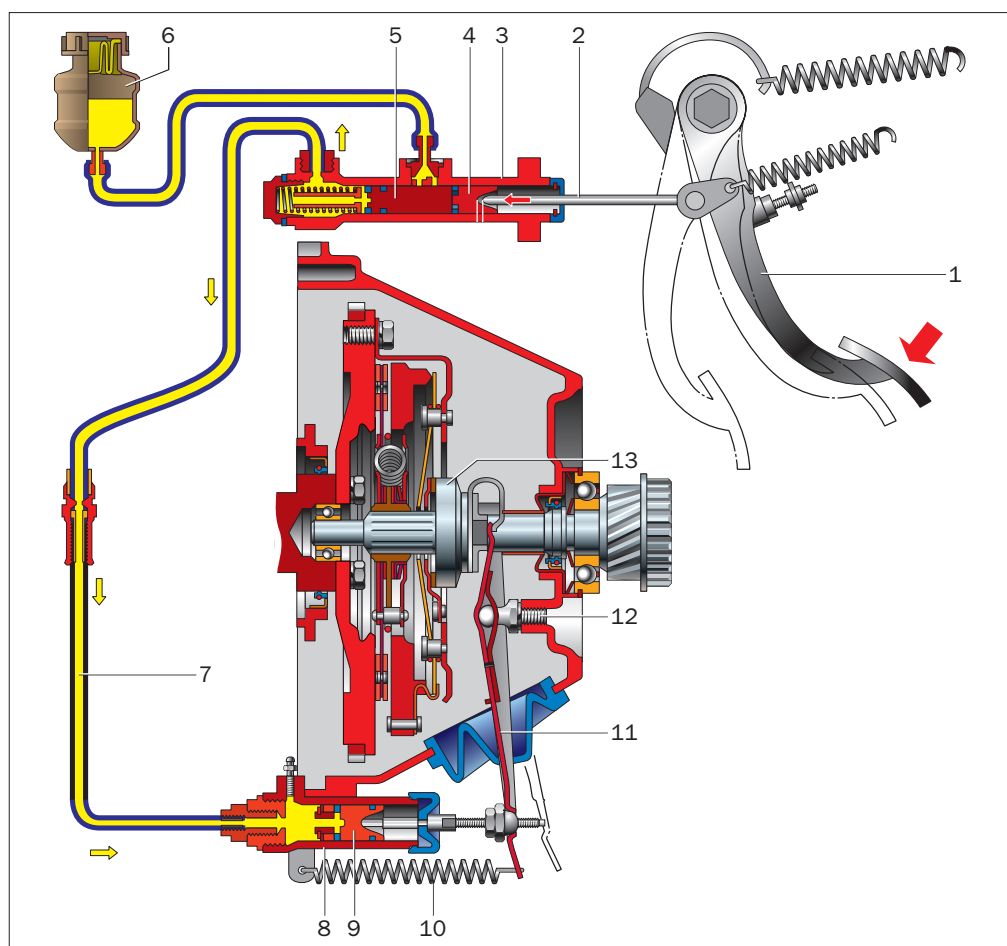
а. Схема гидравлического привода сцепления: 1 — педаль; 2 — толкатель; 3 — главный цилиндр; 4 — поршень толкателя; 5 — поршень главного цилиндра; 6 — бачок; 7 — трубопровод; 8 — рабочий цилиндр; 9 — поршень; 10 — пружина; 11 — вилка; 12 — опора вилки; 13 — выжимной подшипник
